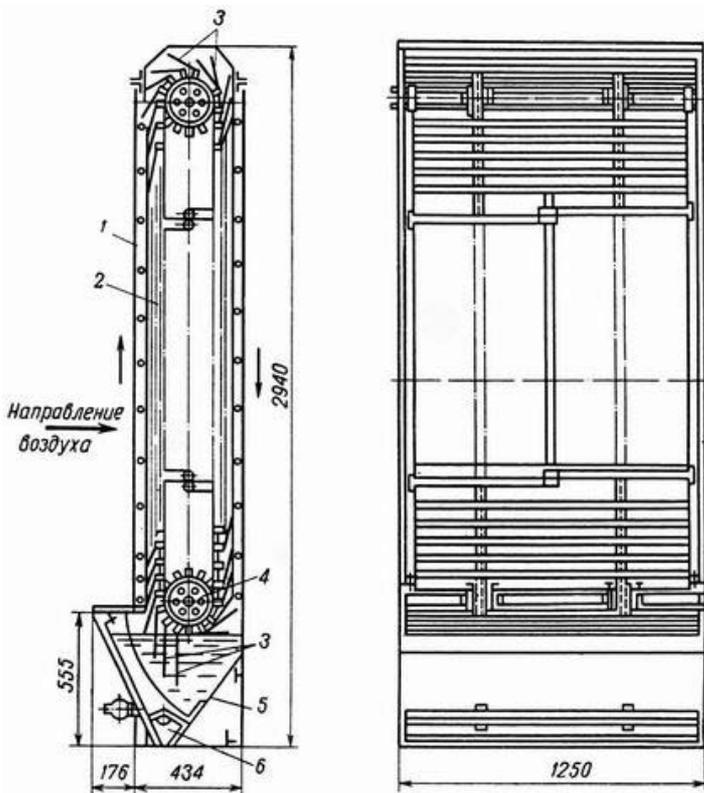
Самоочищающийся масляный фильтр: 1 - каркас; 2 - цепь; 3 - шторка из стальной сетки; 4 - зубчатый валик; 5 - ванна; 6 - бункер для шлама
